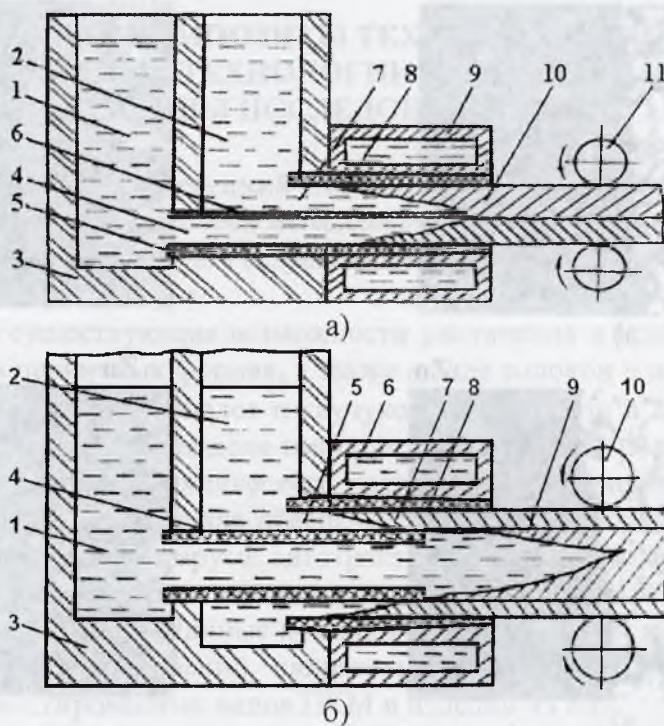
(а) Схема установки для получения прямоугольных биметаллических заготовок: 1 – металл 1; 2 – металл 2; 3 – металлоприемник; 4 – нижний канал; 5 – нижняя графитовая вставка; 6 – пластина; 7 – верхний канал; 8 – верхняя графитовая вставка; 9 – водоохлаждаемый корпус кристаллизатора; 10 – биметаллическая отливка; 11 – тянущие клетки. (б) Схема установки для получения цилиндрических биметаллических заготовок: 1 – металл 1; 2 – металл 2; 3 – двухсекционный металлоприемник; 4 – металлопровод; 5 – кольцевой канал; 6 – водоохлаждаемый корпус кристаллизатора; 7 – полая заготовка металла 2; 8 – графитовая втулка; 9 – биметаллическая отливка; 10 – вытягивающее устройство
